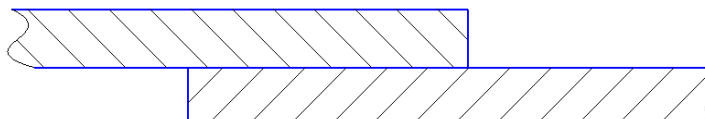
Форма подготовленных кромок под сварку для нахлесточных соединений [20].
